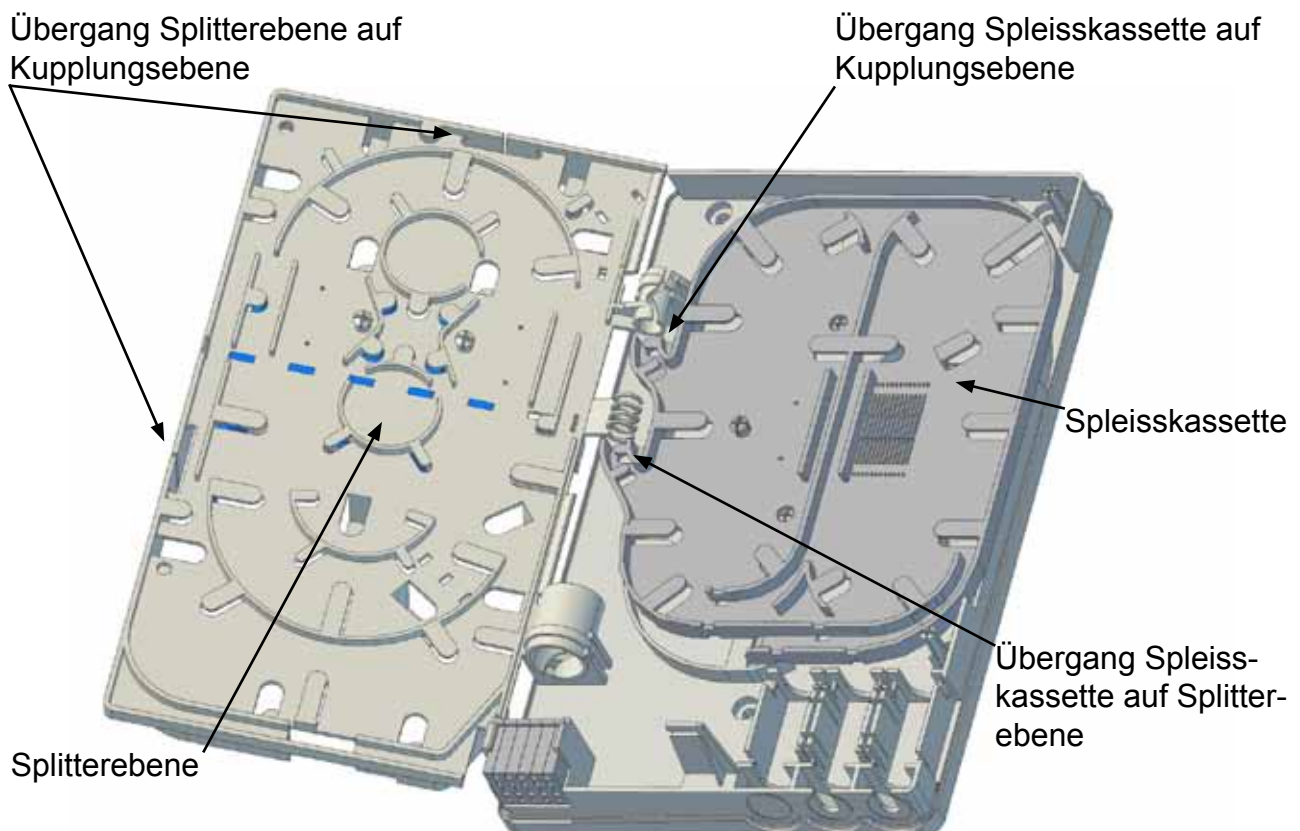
Gehäuse aufgeklappt (Variante ohne PG Verschraubungen)
